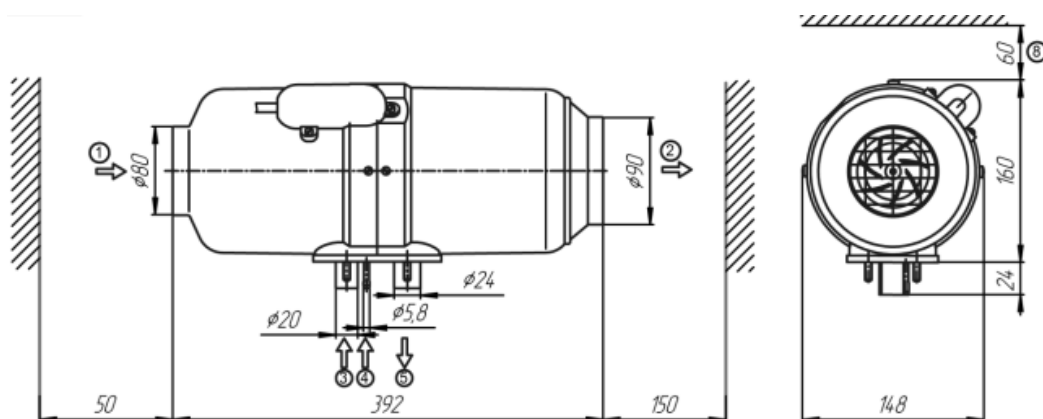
Габаритные размеры подогревателя «Планар 4ДМ2»
